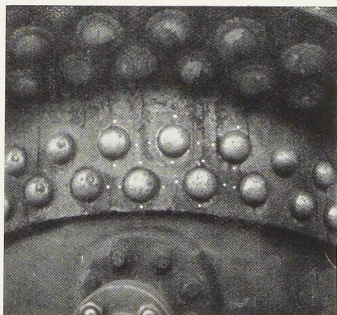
Détail d'un cylindre de cracking rivé soudé. Il reste 2 rangées de rivets et un joint à souder.
